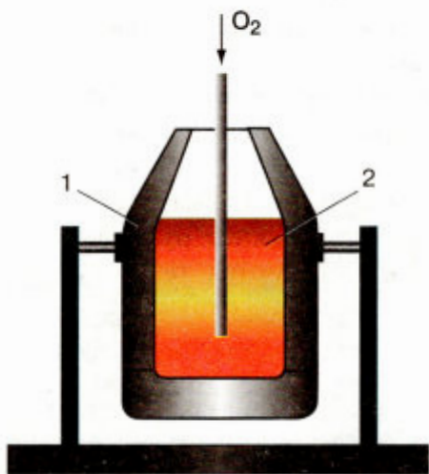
Кислородный конвертер: 1 — огнеупорный материал; 2 — расплавленный металл
